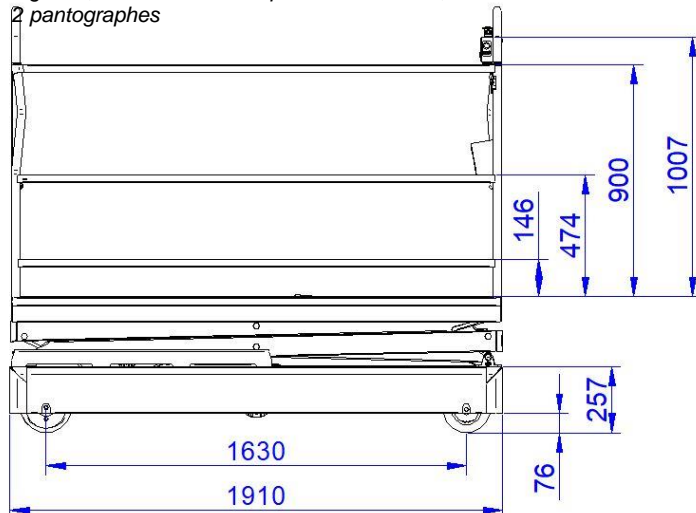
; Dimensions de la longueur en mm, 2 pantographes
